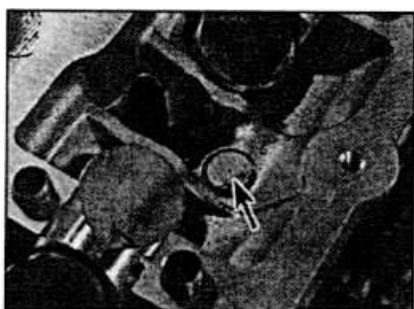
D.32. Заглушка масляной магистрали головки блока цилиндров.
